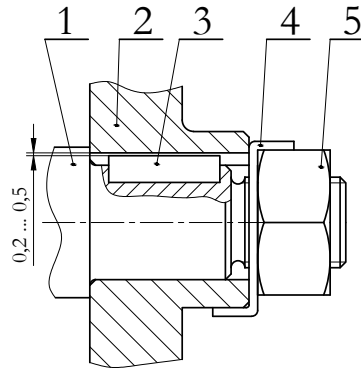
Befestigung mit einer Schraubenmutter auf einem Gewindeendzapfen
